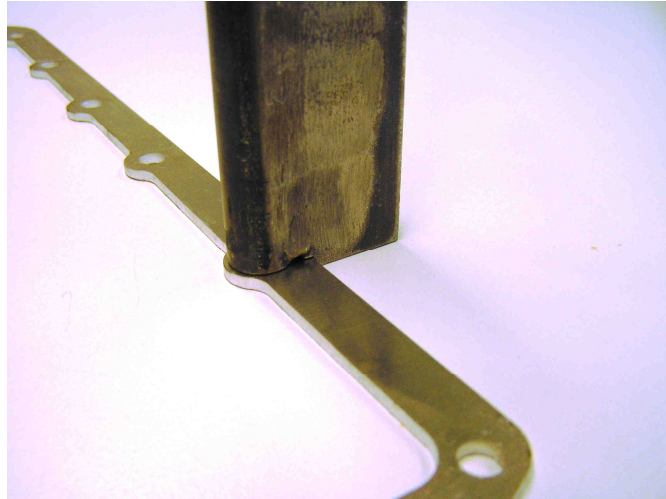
Anwendung des Werkzeugs vor dem Schweißen
